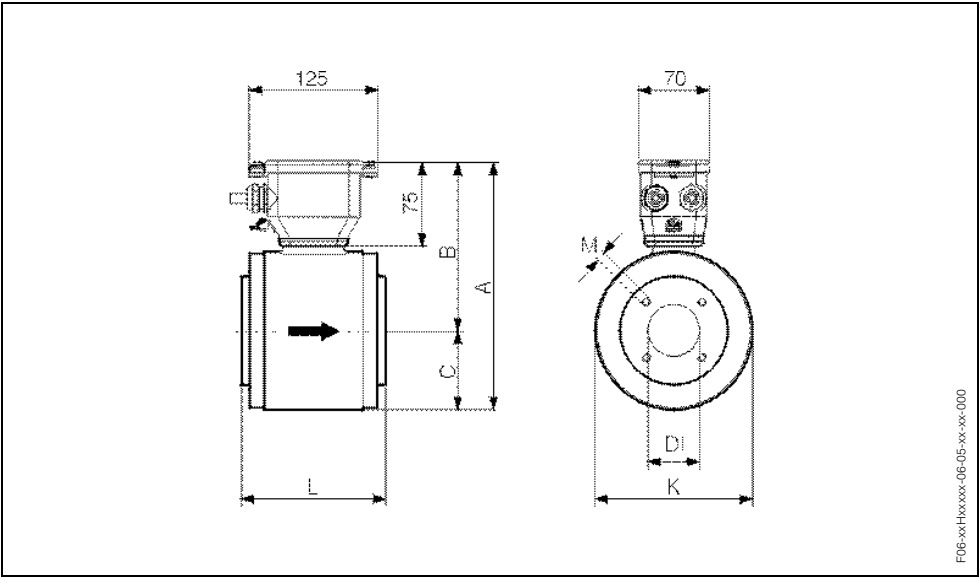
Dimensiones Promag H / DN 40...100 (versión separada)
